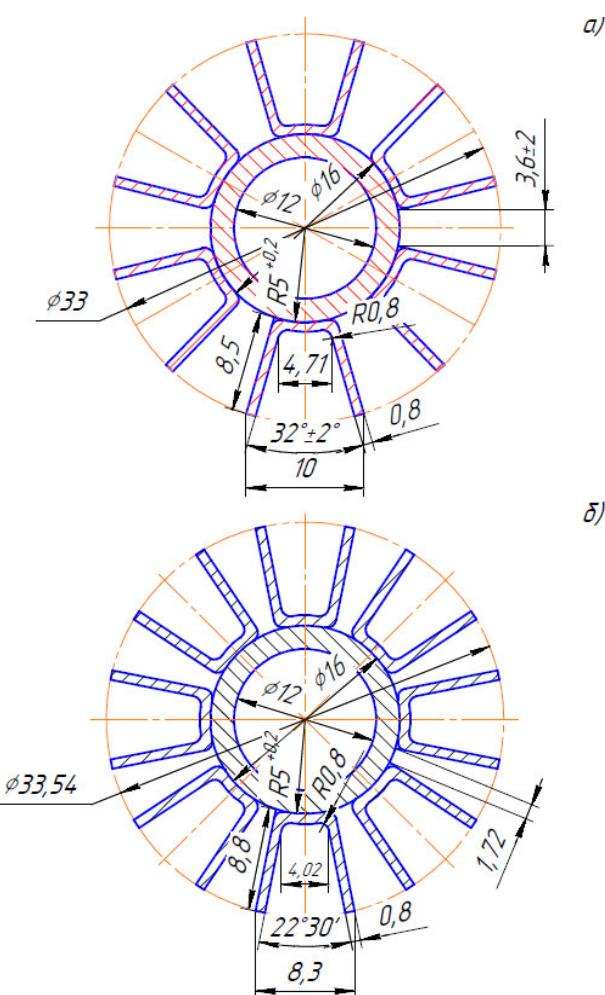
Поперечное сечение теплообменных труб: а) с шестью двойными П-образными ребрами; б) с восьмью двойными П-образными ребрами [Cross section of heat exchange tubes: a) with six double U-shaped ribs; b) with eight double U-shaped ribs]
